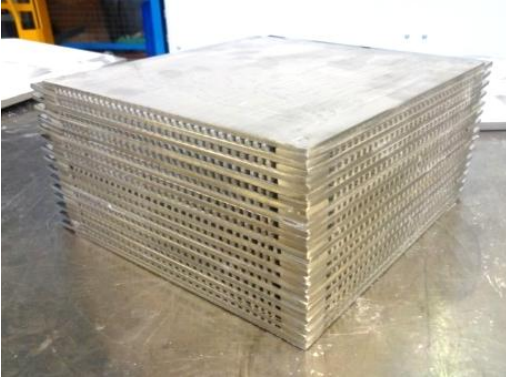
Núcleo de aço inoxidável AISI 316L após o processo de soldagem por difusão.
